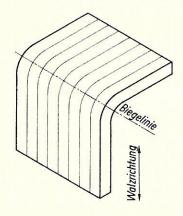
Biegelinie rechtwinklig zur Walzrichtung
